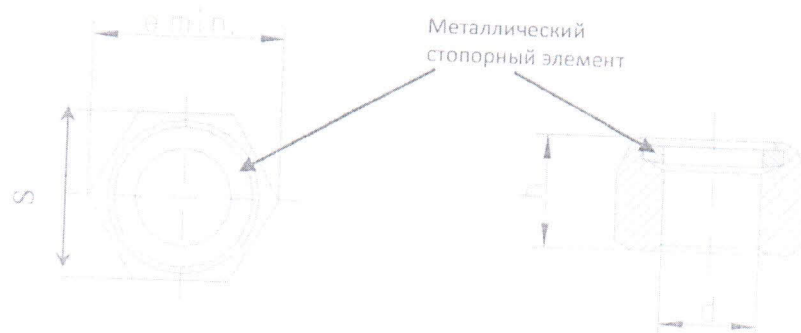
Конструкция и обозначение геометрических размеров FS-гайки
